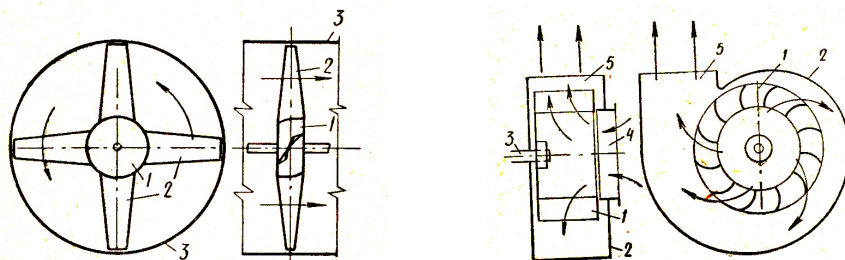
Вентилятори: а – осьовий: 1 – колесо, 2 – лопатки, 3 – корпус; б – відцентровий: 1 – лопаткове колесо, 2 – корпус, 3 – привід, 4 – вхідний отвір, 5 – випускний отвір.
